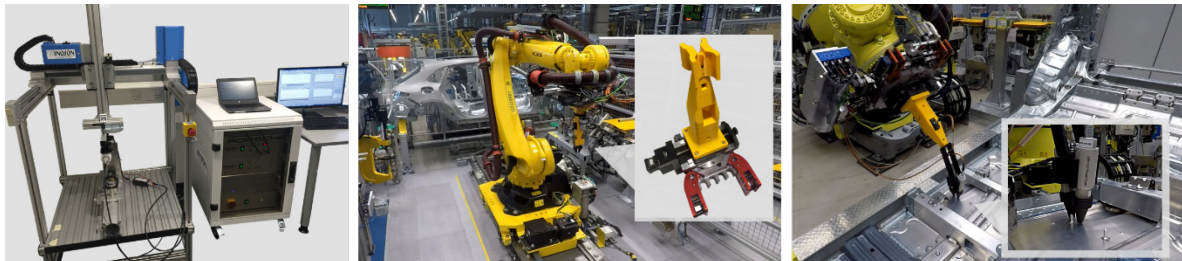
ZfP von Widerstandspunkt- und Bolzenschweißverbindungen am Manipulator und am Industrieroboter
